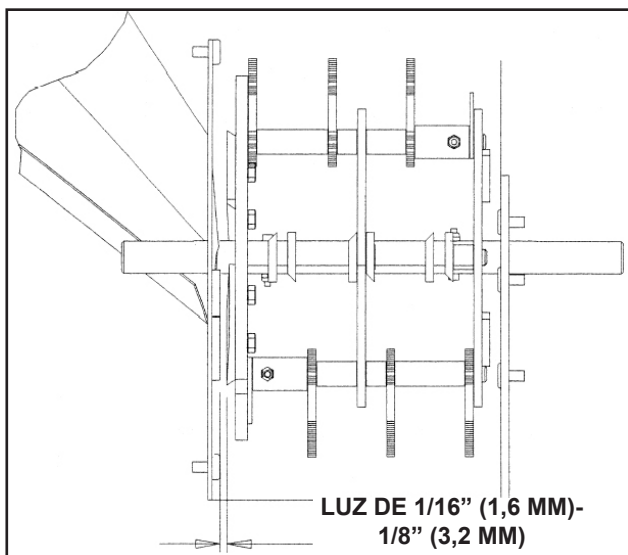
Cuchilla chipeadora y holgura del bloque
